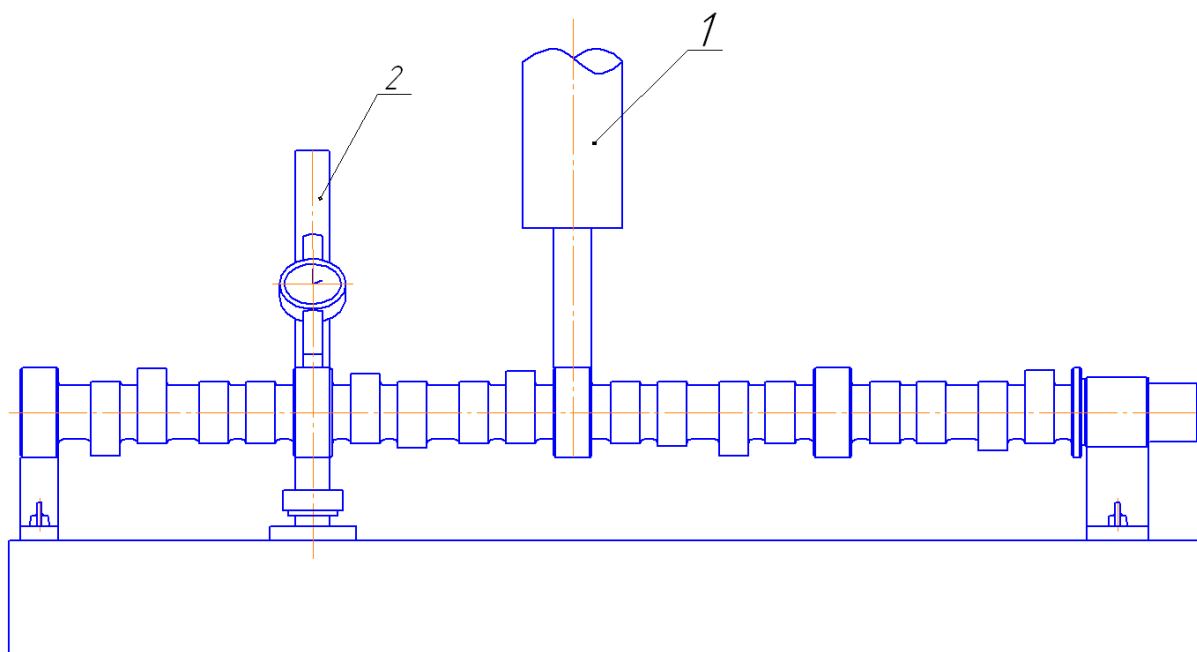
Схема модифицированного приспособления для измерения и правки прогиба распределительного вала: 1- шток пресса; 2- стойка часового индикатора.
